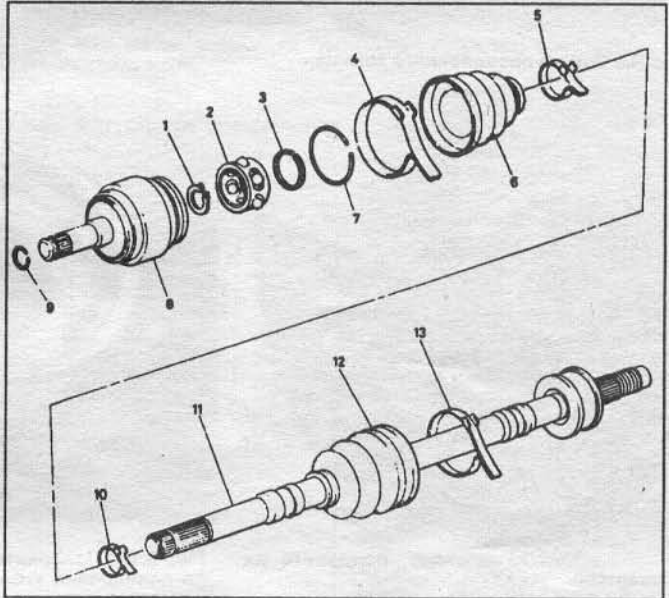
в Разборка внутреннего ШРУСа: 1 - стопорное кольцо; 2 - сепаратор; 3 - упорное кольцо; 4 - зажим; 5 - зажим; 6 - чехол; 7 - кольцо; 8 - корпус шарнира; 9 - стопорное кольцо; 10 - зажим; 11 - приводной вал; 12 - чехол; 13 - зажим.
